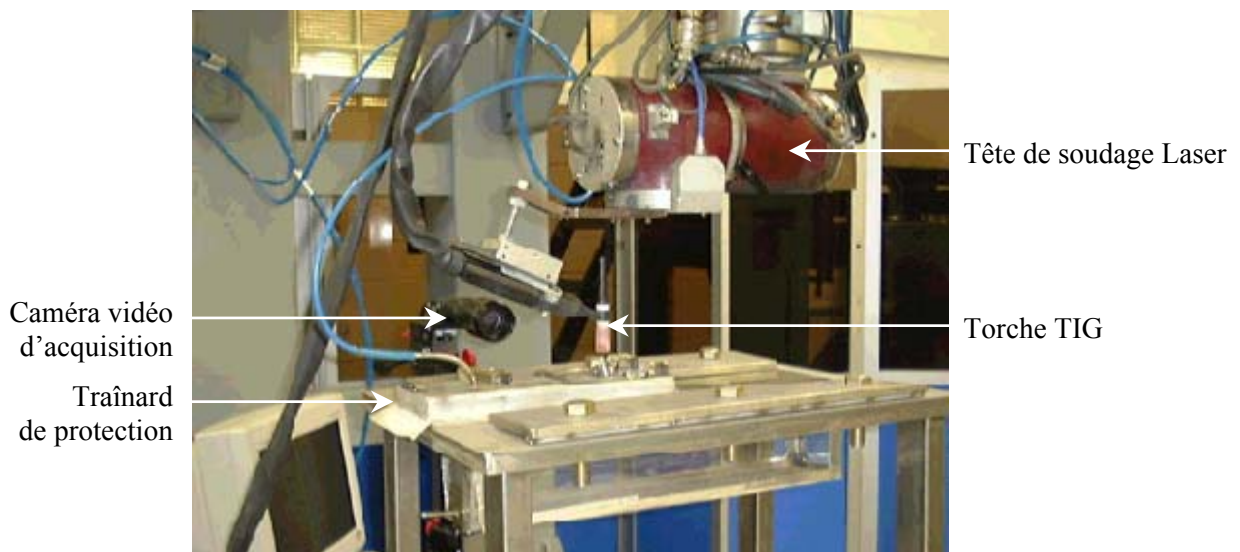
Torche de soudage fixée à la tête Laser et système d'acquisition vidéo
